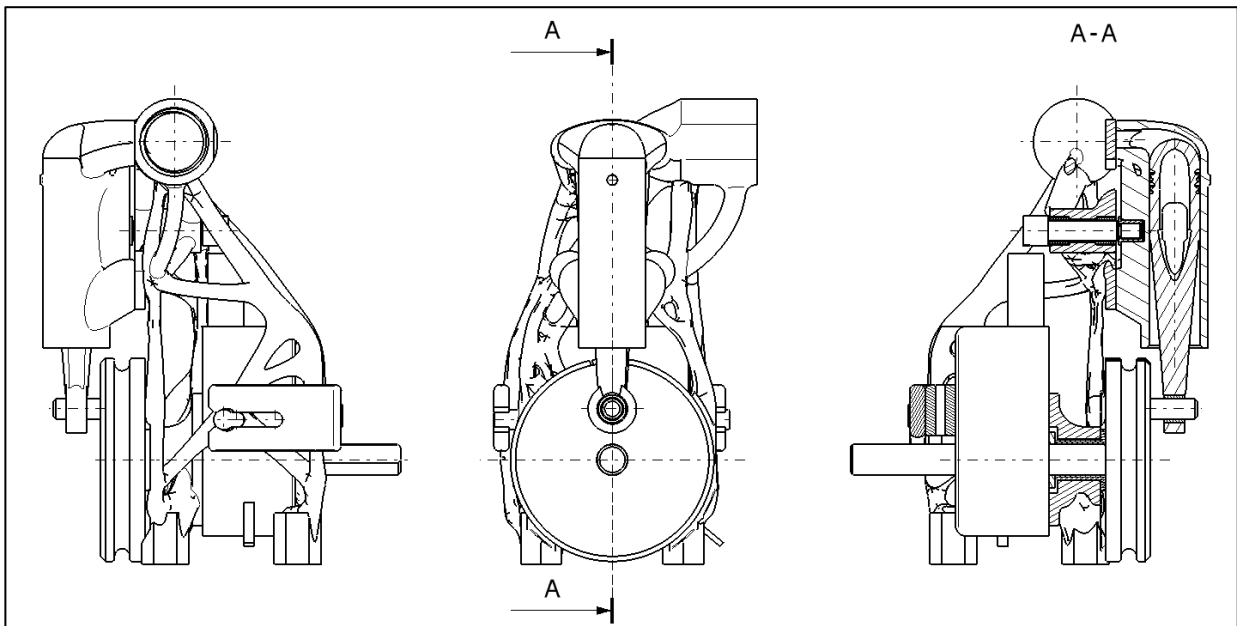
Extrait du dessin d'ensemble du moteur Eam3 de l'étude de cas « moteur à air »
